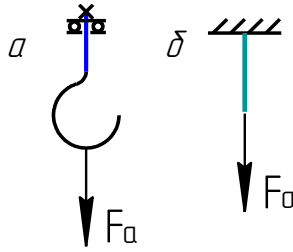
Вантажний гак і його розрахункова схема
